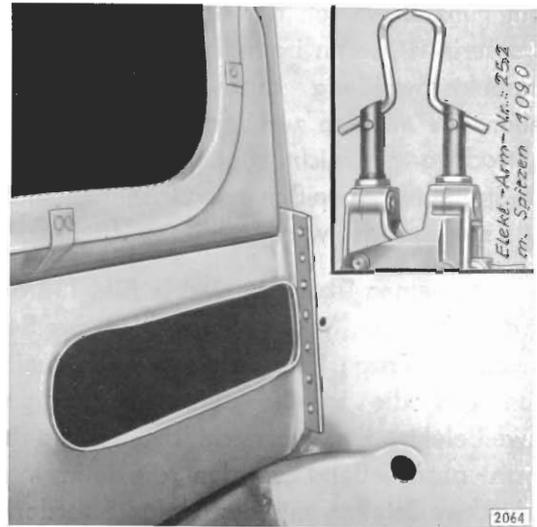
Seitenwand im Kofferraum an Flansch der Kofferraumrückwand zangenpunktgeschweißt
